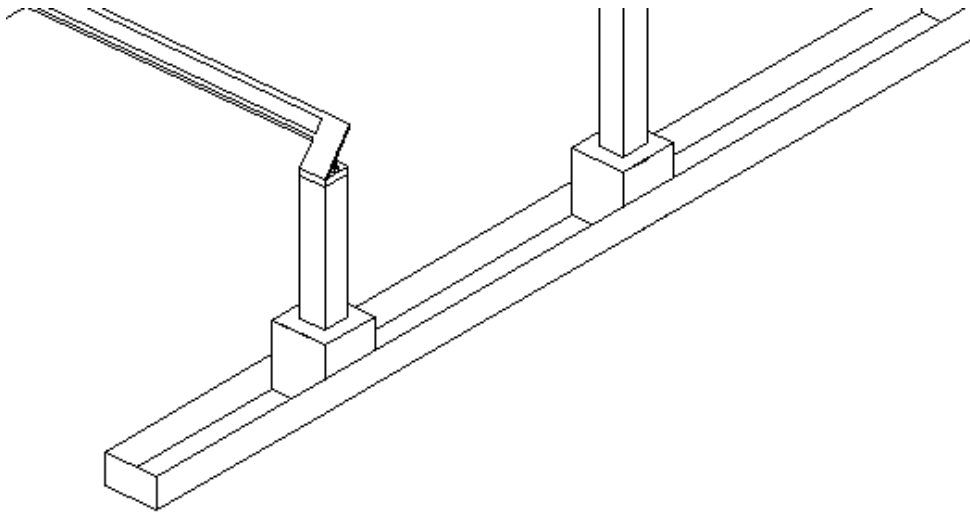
Raíles del soporte para facilitar la colocación. Fuente: Propia
